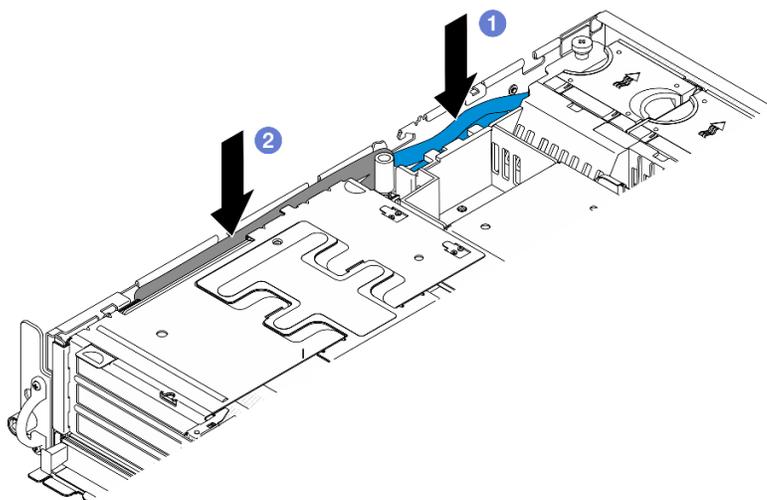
Disposición de los cables de señal de la tarjeta de expansión PCIe 1
